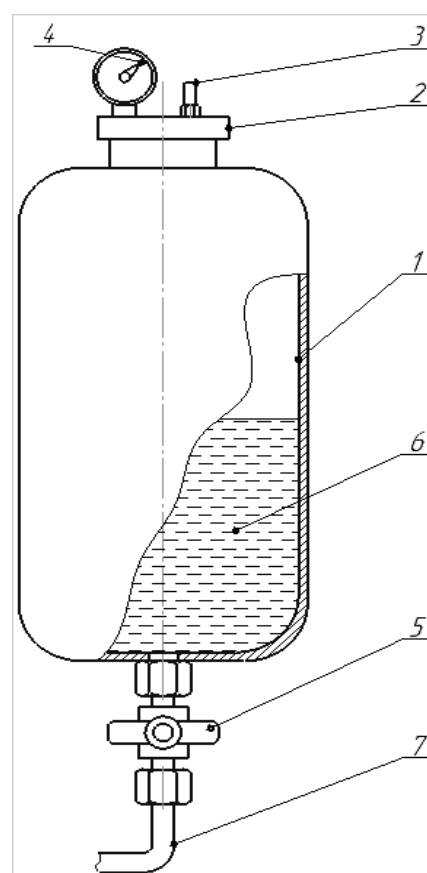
Общий вид резервуара для жидких масел: 1 – корпус, 2 – крышка заливной горловины, 3 – ниппель для закачки воздуха, 4 – манометр, 5 – кран, 6 – смазочный материал, 7 – раздаточный шланг
